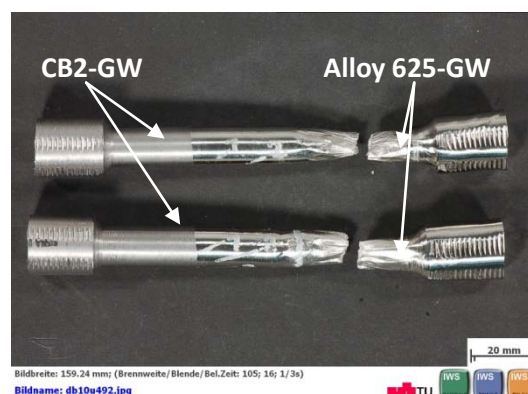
Erste Querzugproben geschweißt mit Stabelektroden. Bruchlage im Grundwerkstoff der Alloy 625.
